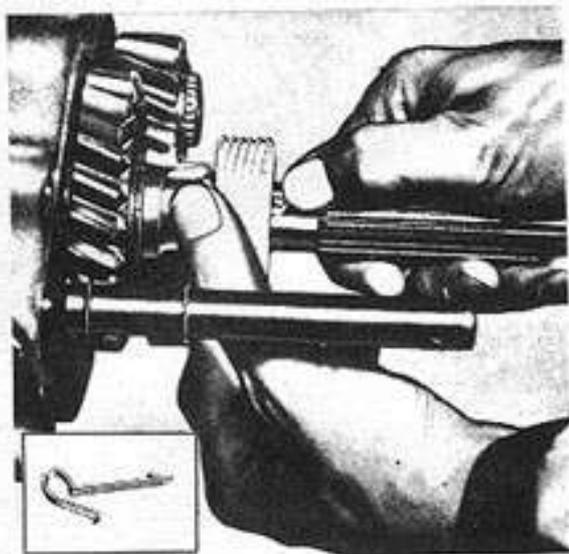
Extracción del engranaje sinfín de accionamiento del cable del velocímetro
